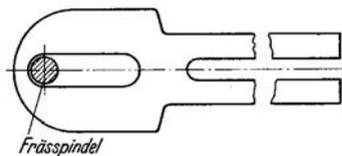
Auf dem Frästisch befestigtes Anlaufstück für Arbeiten an Schablone.
